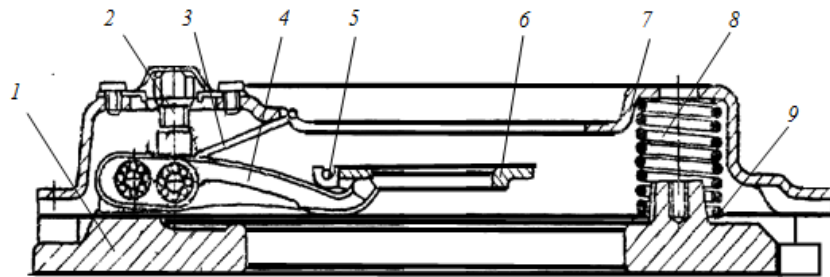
Притискний механізм муфти зчеплення: 1 – натискний диск; 2 – вилка відтискного важеля; 3 пружина упорного кільця; 4 – важіль; 5 – петля пружини; 6 – упорне кільце; 7 – кожух; 8 – натискна пружина; 9 – термоізоляційна шайба
